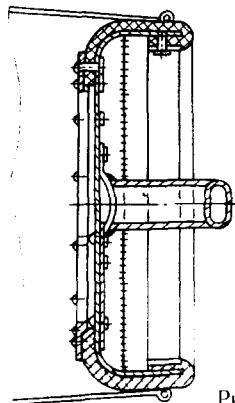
Заглушка на выхлопной патрубок двигателя АИ-9В
